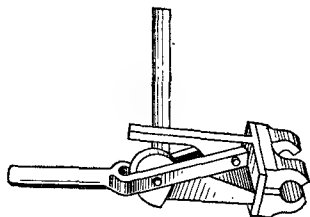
Ручное эксцентриковое приспособление ГМ029А
